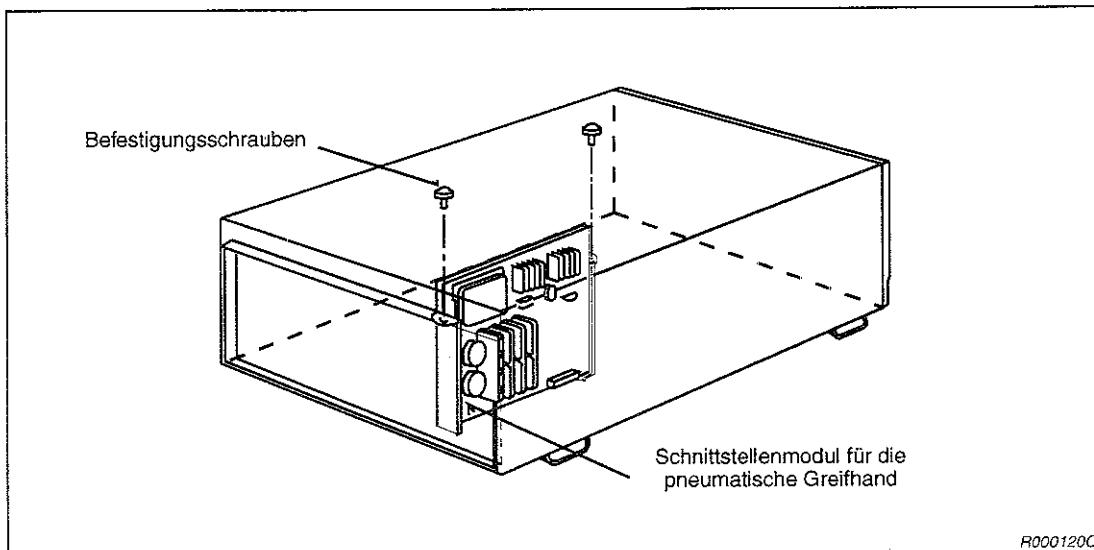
Einbau des Schnittstellenmoduls für die pneumatische Greifhand
